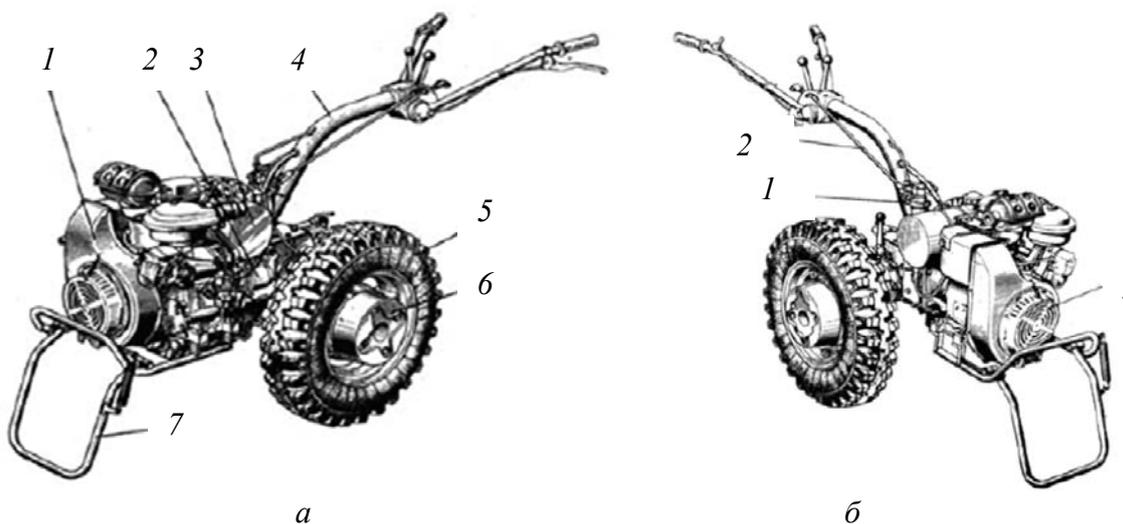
Мотоблок: *а* – вид слева: 1 – двигатель; 2 – силовая передача; 3 – бензобак; 4 – рулевая штанга; 5 – колесо; 6 – груз; 7 – подножка; *б* – вид справа: 1 – рычаг переключения передач; 2 – тяга механизма переключения передач; 3 – ручка запуска
